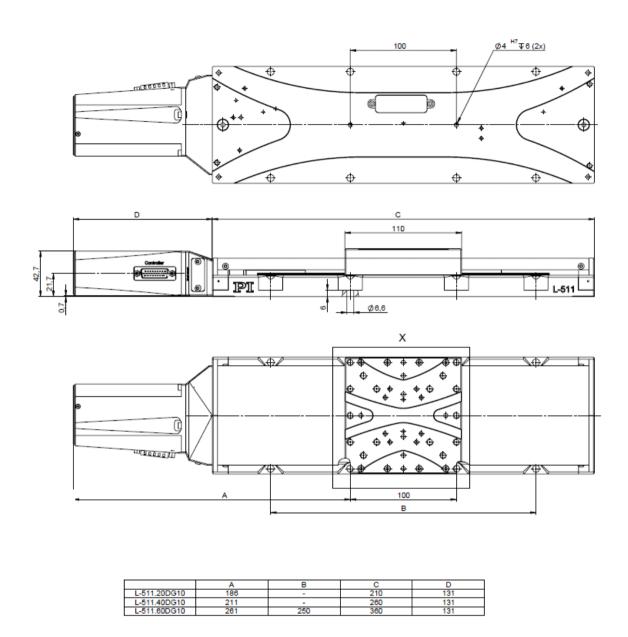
L-511-Versionen mit DC-Getriebemotor, Abmessungen in mm
